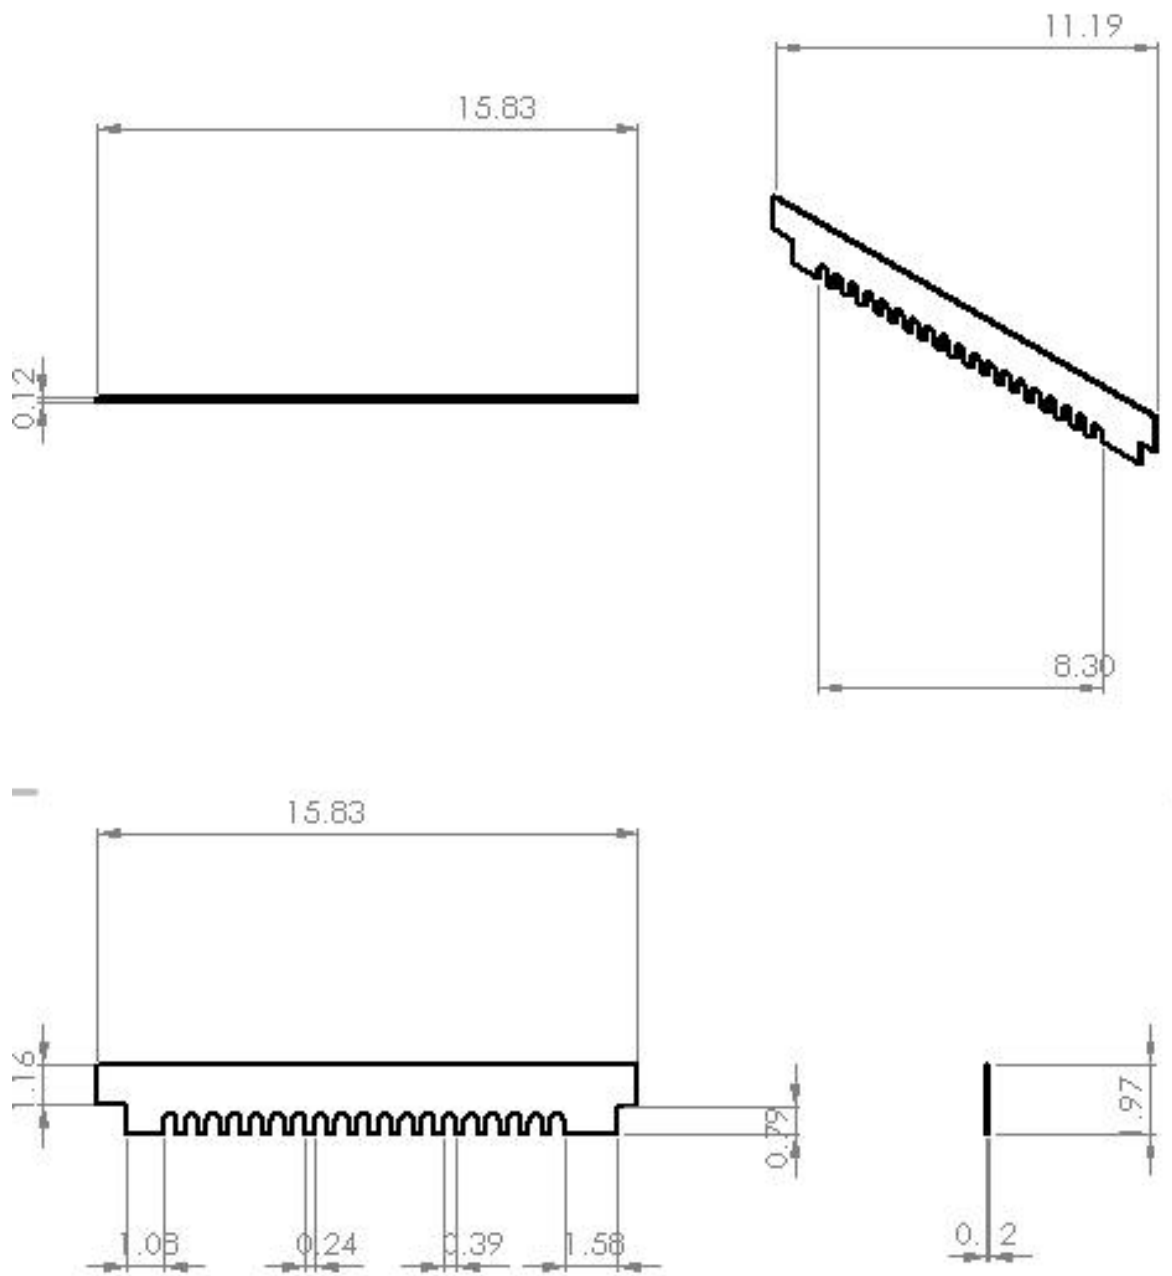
Dimensions de la Grille d'entrée anti- intrusion
